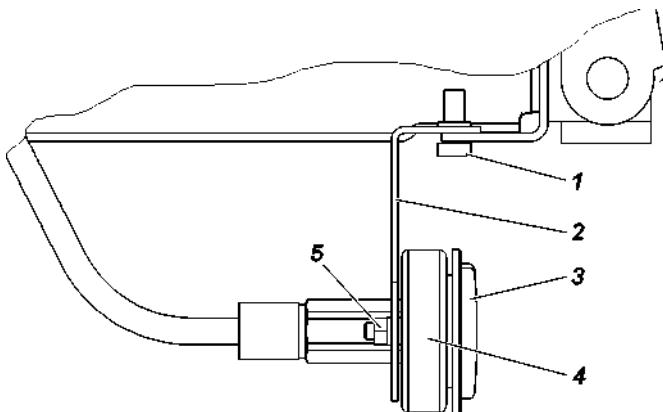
Установка заправочного устройства с поперечным расположением баллона:
